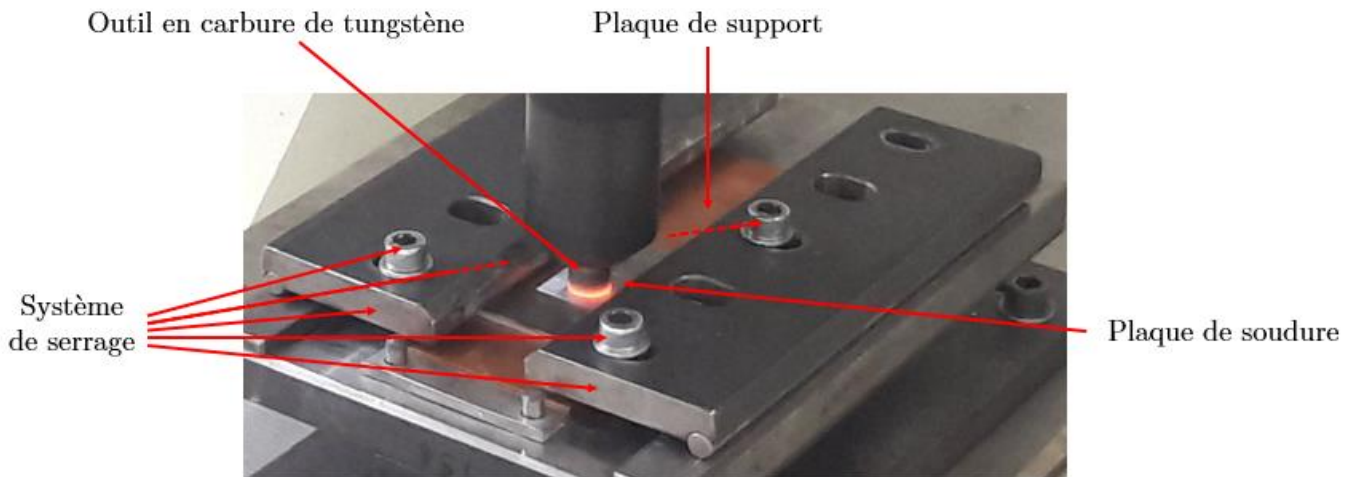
Photo du dispositif lors d'une soudure.
